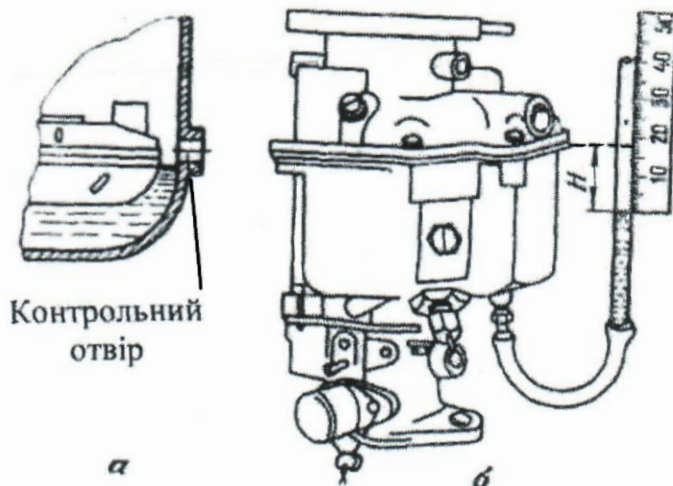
Способи перевірки рівня пального в поплавковій камері карбюратора
